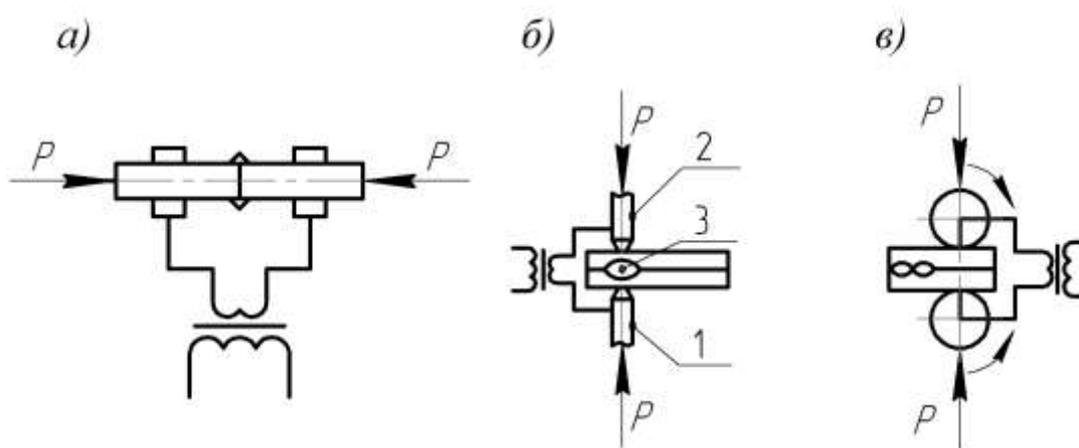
Схемы контактной сварки: а – стыковой; б – точечной; в – шовной; 1 и 2 – электроды; 3 – сварная точка
